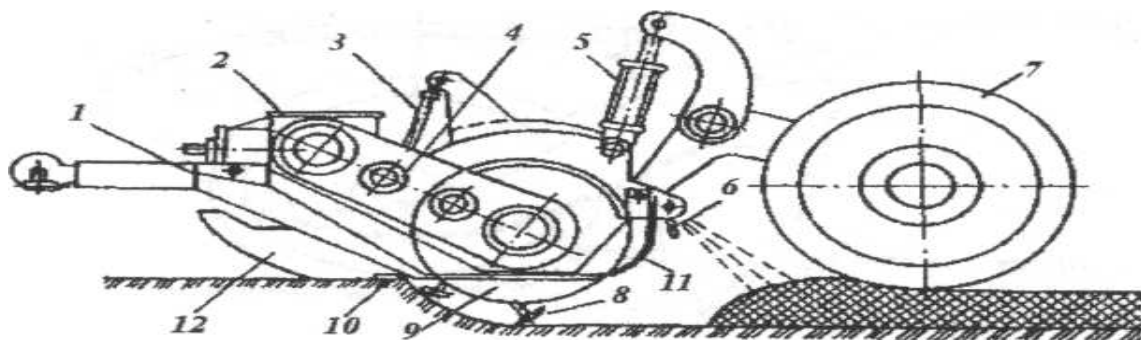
Схема машины лесной фрезерной МЛФ-0,8:
